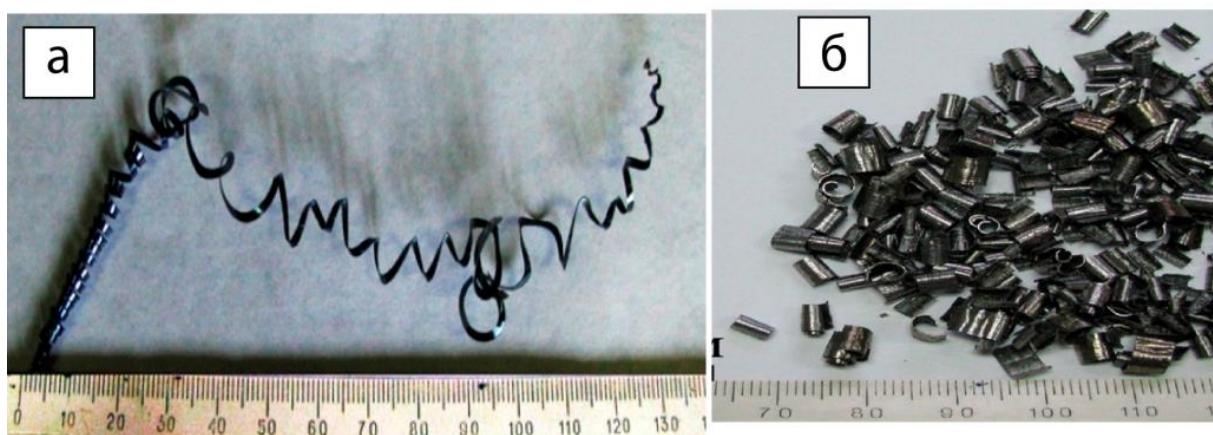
Вигляд стружки після механічної обробки зразка роторної сталі: (а) – на сухо; (б) – із ЗОР
